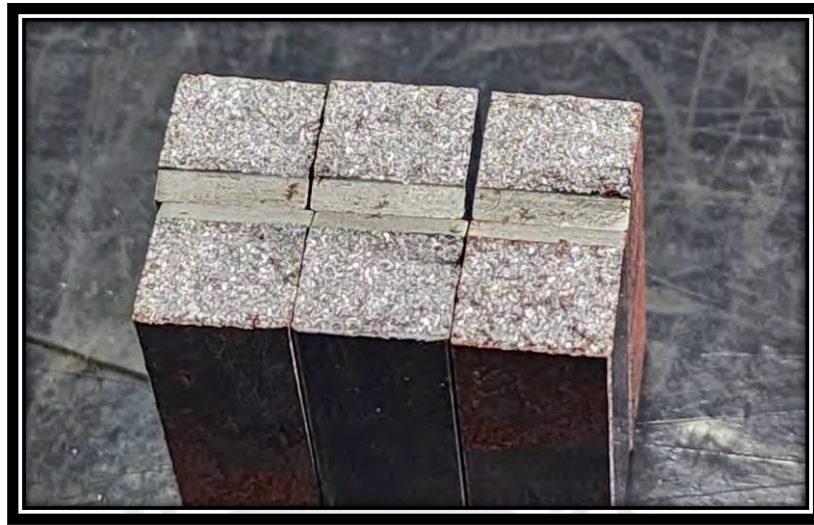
14. *Probetas fracturadas en el ensayo de impacto
